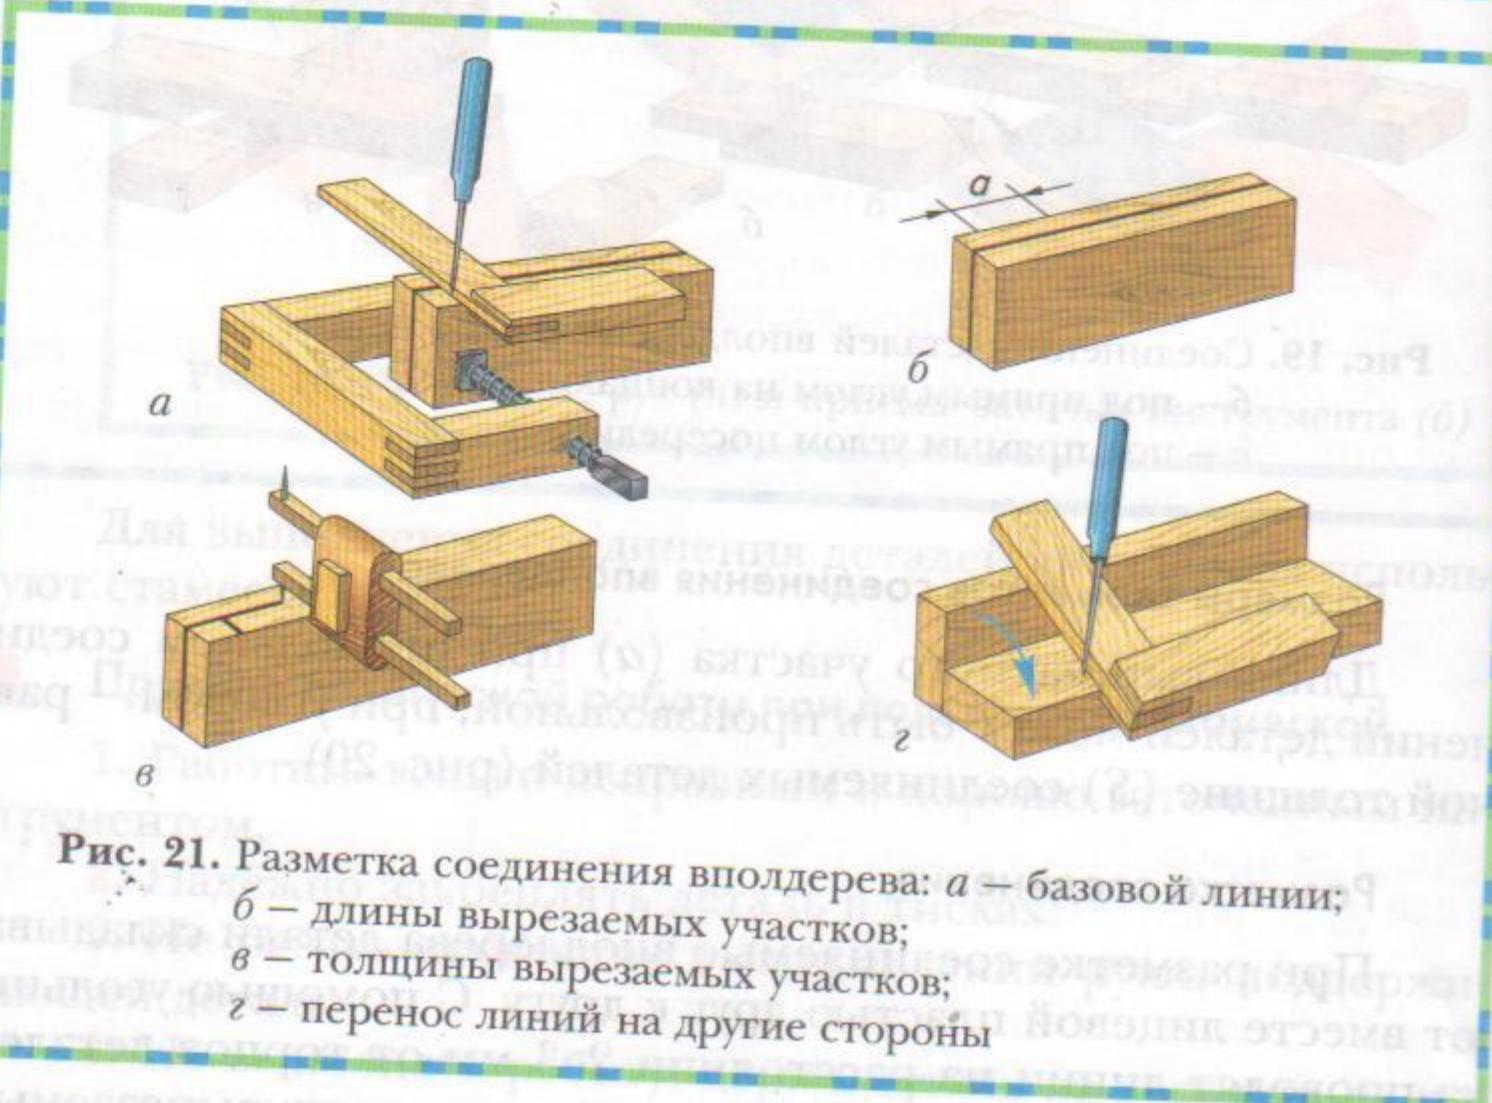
Разметка соединения вполдерева: а – базовой линии;
